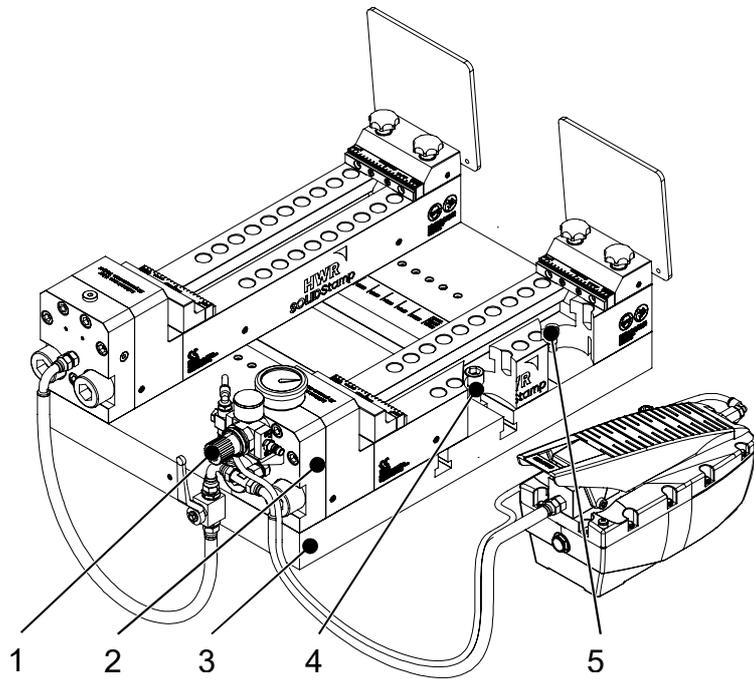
Sfiato dell'unità di stampaggio SOLIDStamp
